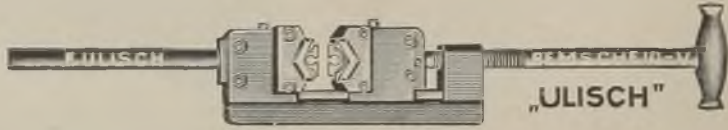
Rohrab Schneider mit zwei Fräsmessern. (Werkzeugfabrik Fedor Uliſch, Remscheid.)
